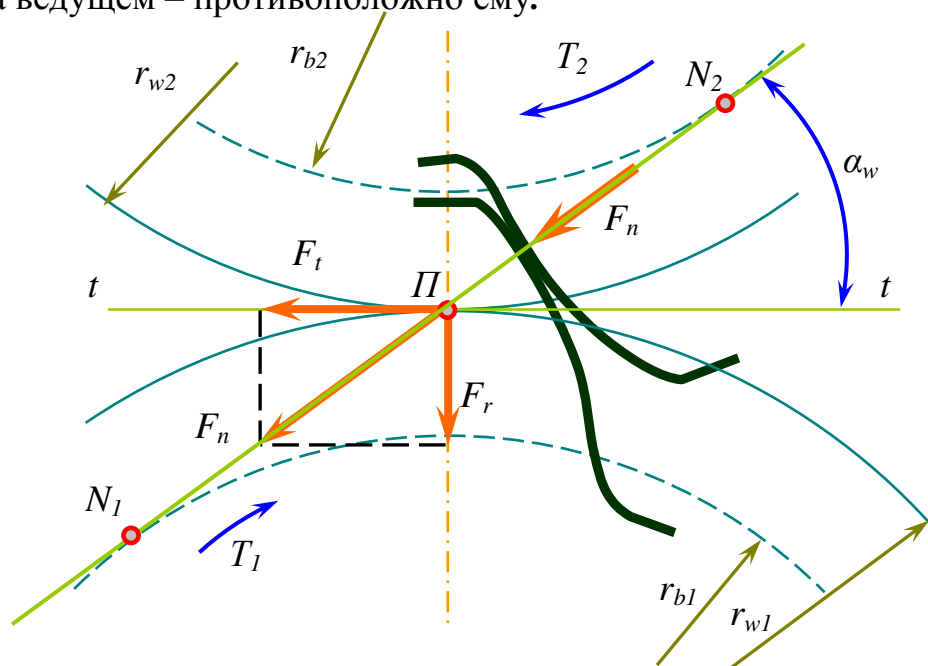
Схема сил в зацеплении прямозубой цилиндрической передачи
